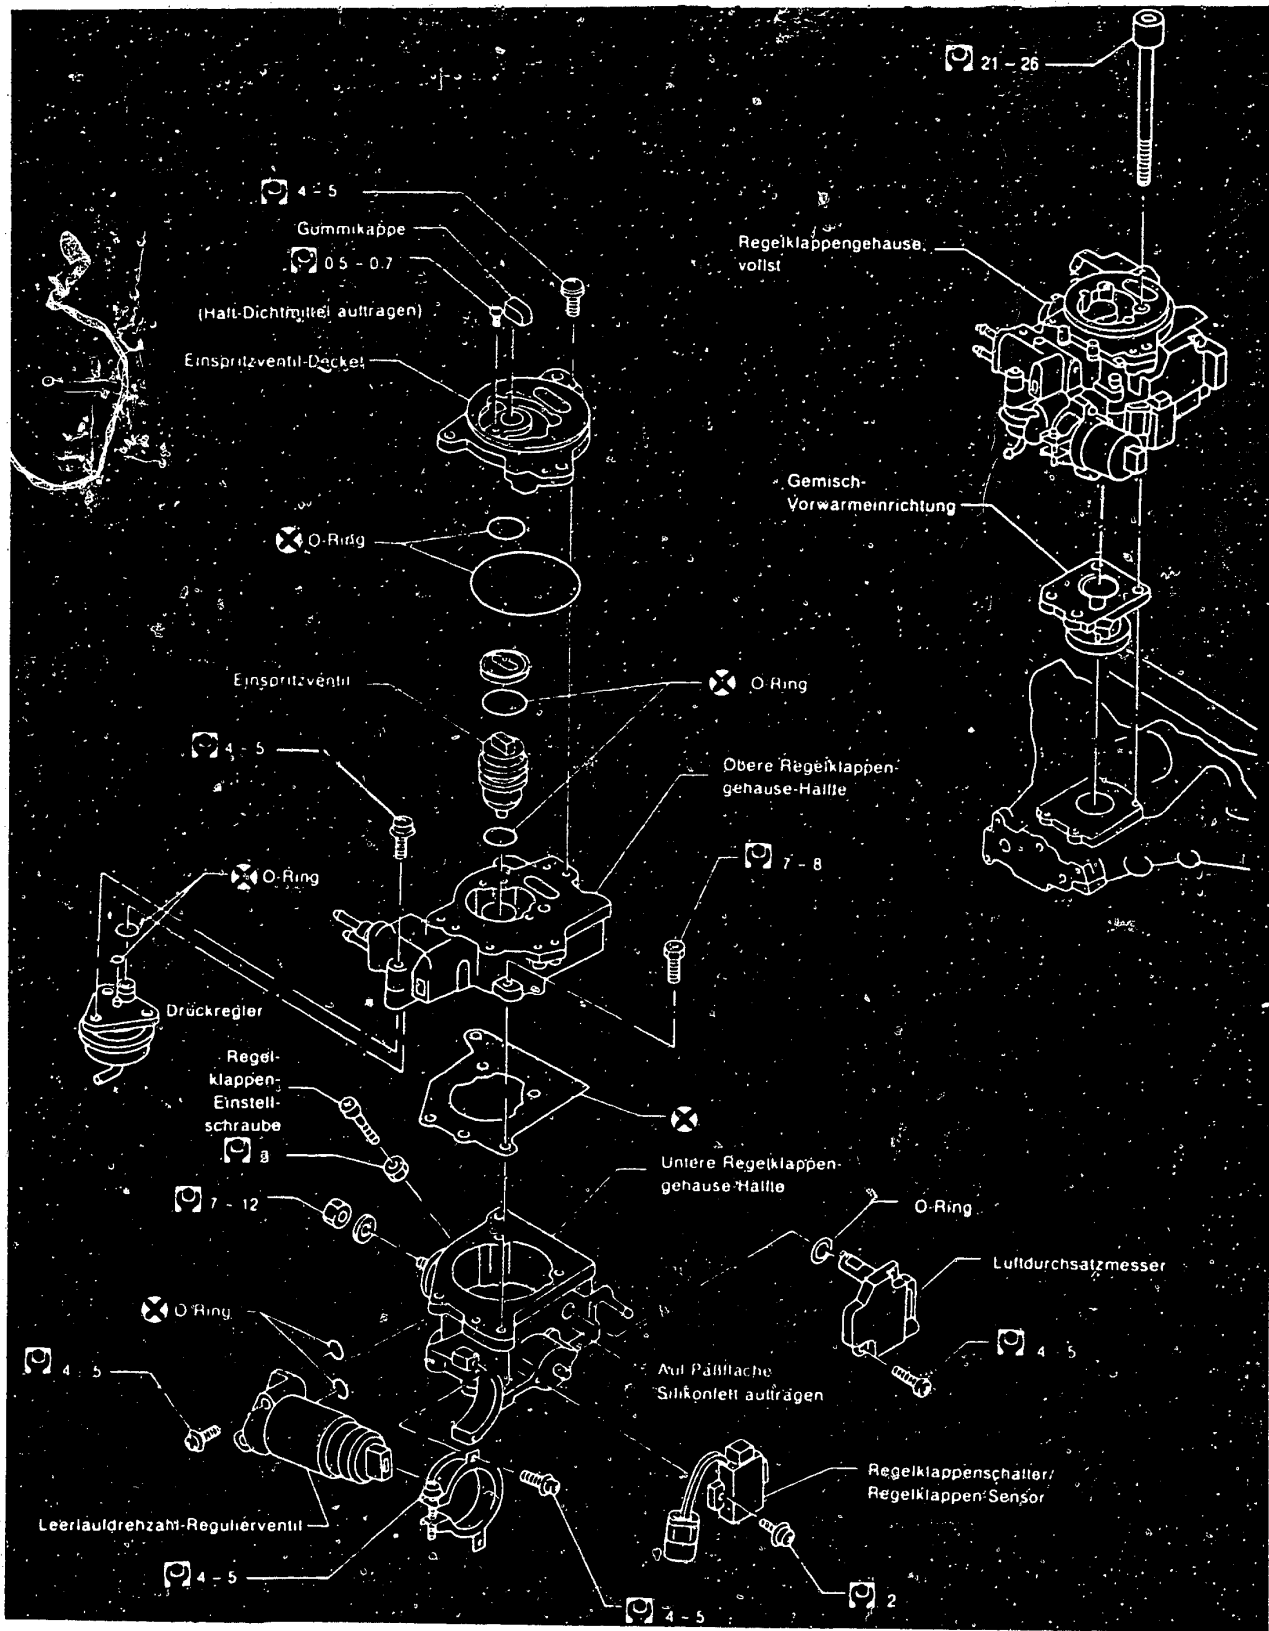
Einzelteile des Drosselklappengehauses der Einspritzanlage in richtiger Montageanordnung. Schlüsselsignet=Schraubenanzugsdrehmoment in Nm.
